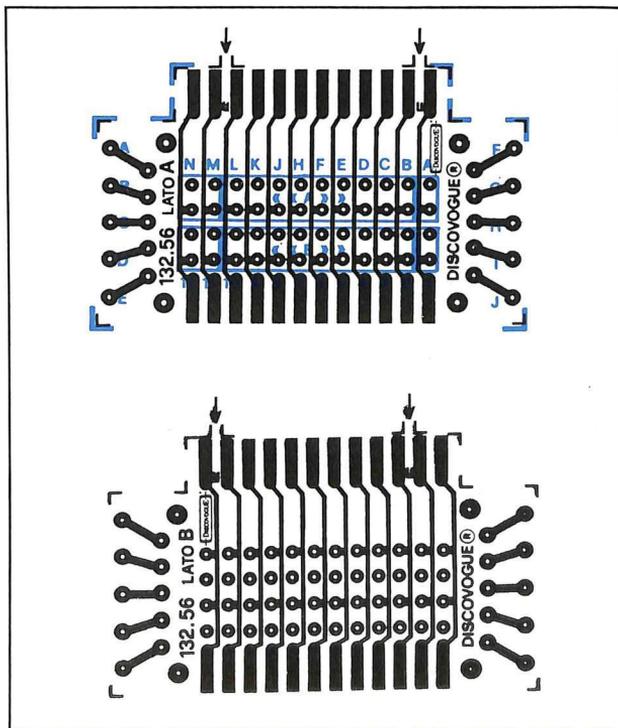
Piste conduttrici del lato A e B del circuito stampato portante e montaggio componenti sul lato A.
